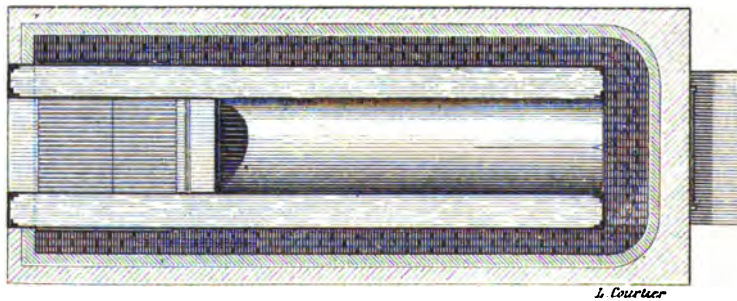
Chaudière de Cornouailles (coupe horizontale).
